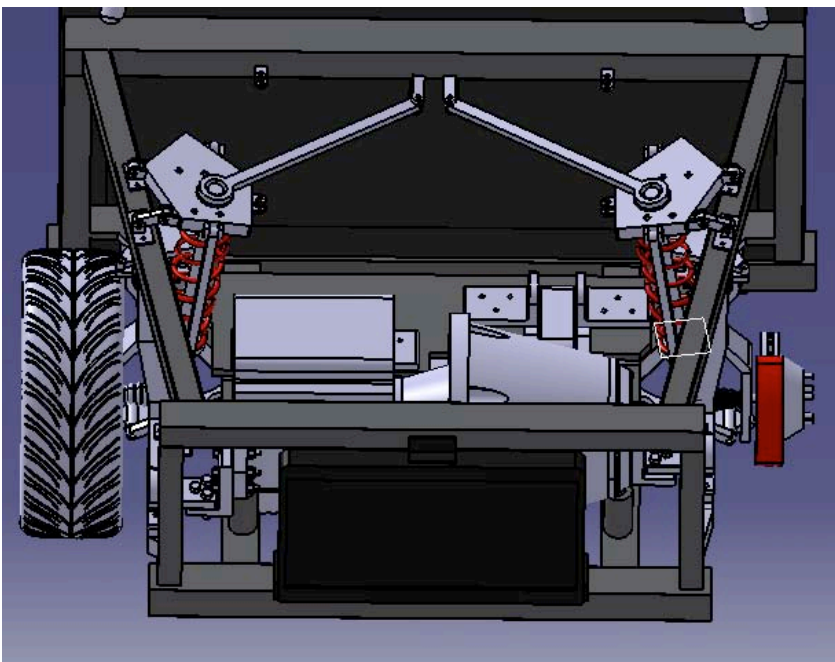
Vista dall'alto del fissaggio duomi anteriori al telaio.
